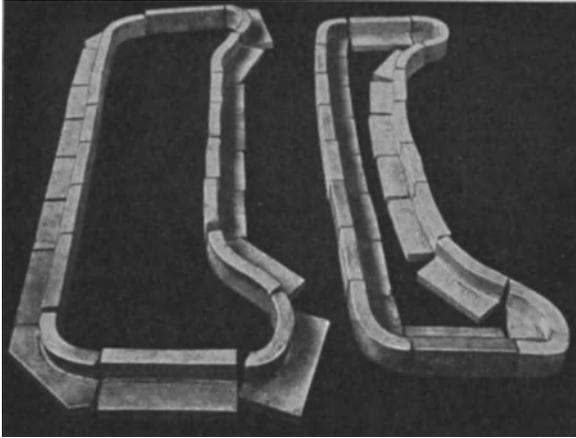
Befestigung des Stahlbesatzes durch Schweißen. Einzelteile eines Schnittes vor dem elektrischen Verschweißen.
